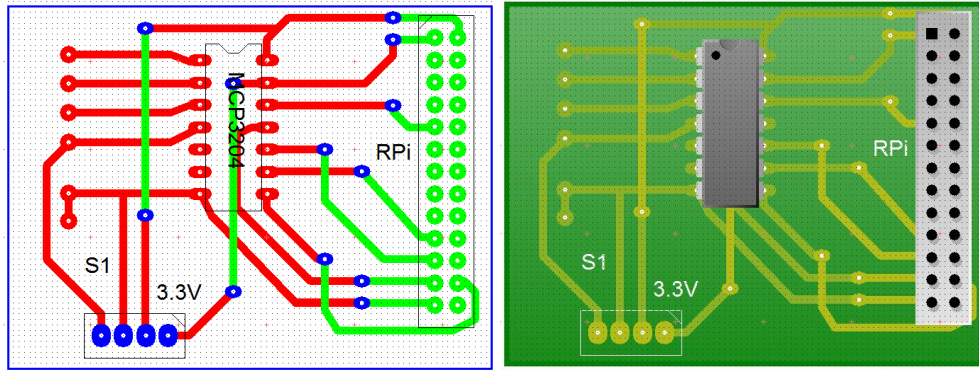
DISEÑO DEL PCB DEL ADC
